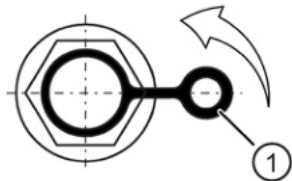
Druckentlüftungsventil mit Sicherungsglasche
